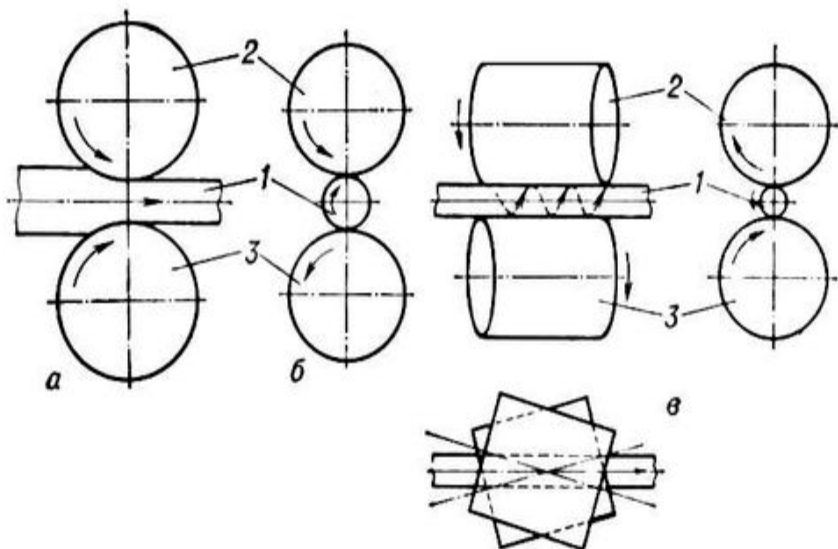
Схемы продольной (а), поперечной (б) и винтовой (в) прокатки: 1— заготовка; 2, 3 — валки
